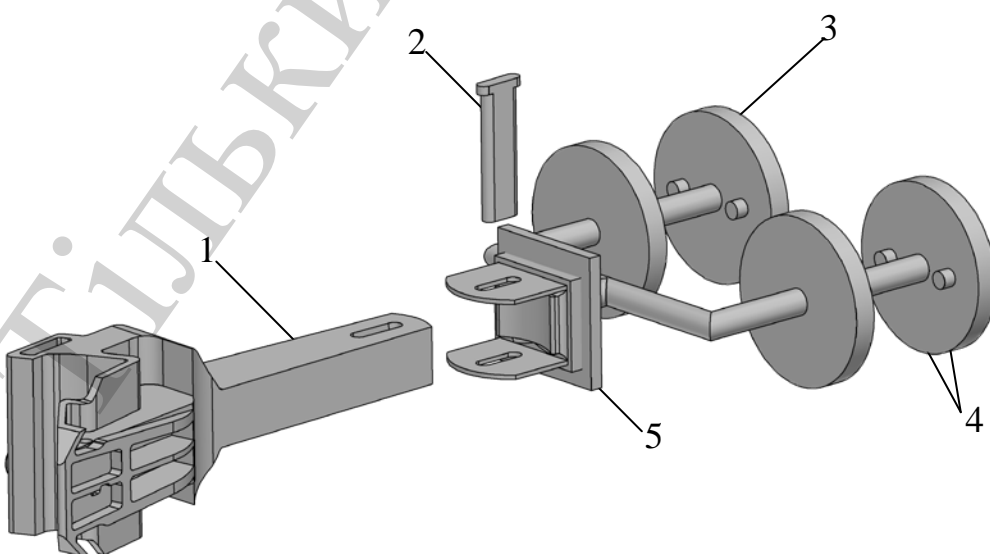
Концепт упряжного пристрою автозчепу: 1 – корпус автозчепу; 2 – клин; 3 – поршень; 4 – дросельні клапани; 5 – упорна планка
